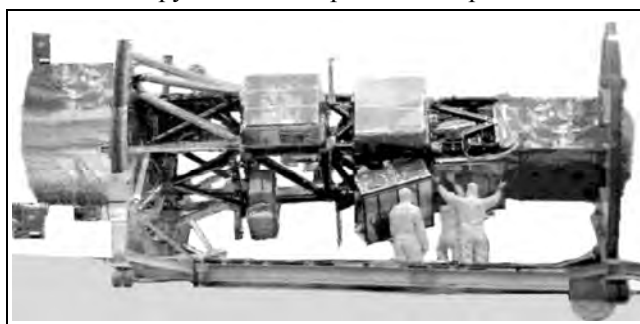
Конструкция КА Lacrosse/ONYX в процессе сборки
